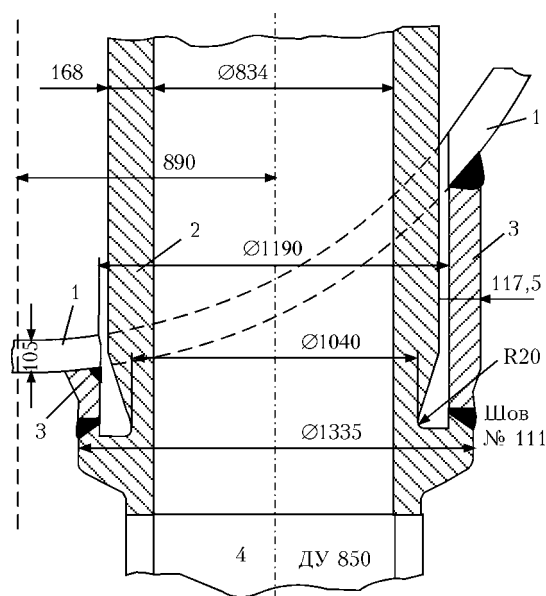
Схема расположения сварного шва № 111: 1 — корпус; 2 — коллектор; 3 — патрубок; 4 — главный циркуляционный трубопровод ДУ-850; 5 — карман
